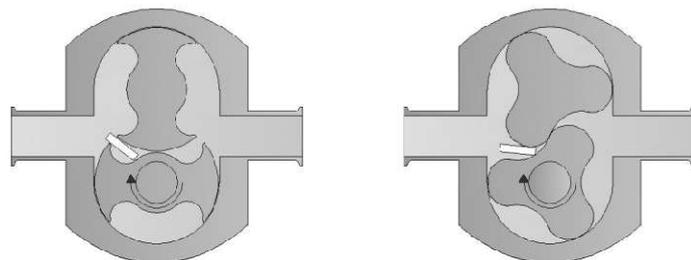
Serrer le boulon du rotor (rotor inférieur)
